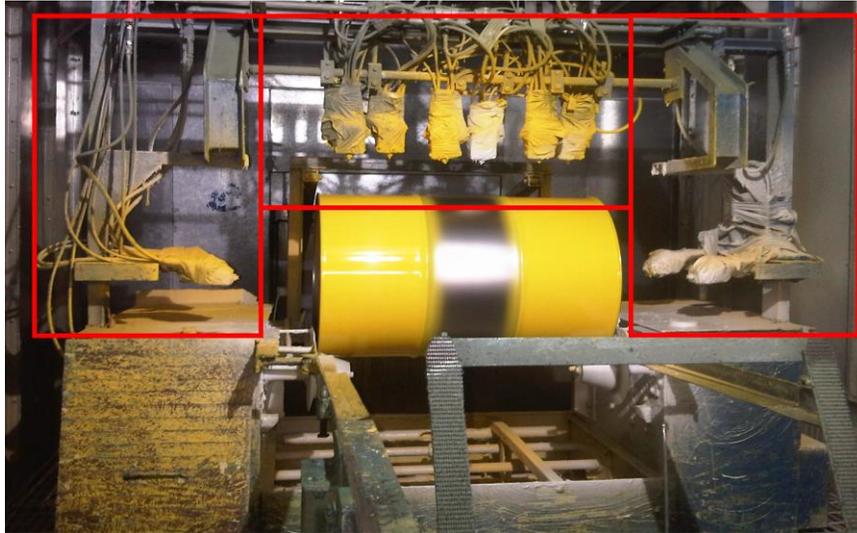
Estructura de soporte de pistolas de aplicación de pintura.
